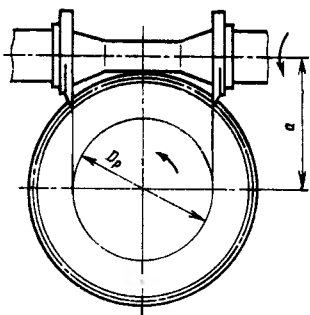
Схема двузубой фрезы-летучки для нарезания колеса прецизионной глобоидной передачи
